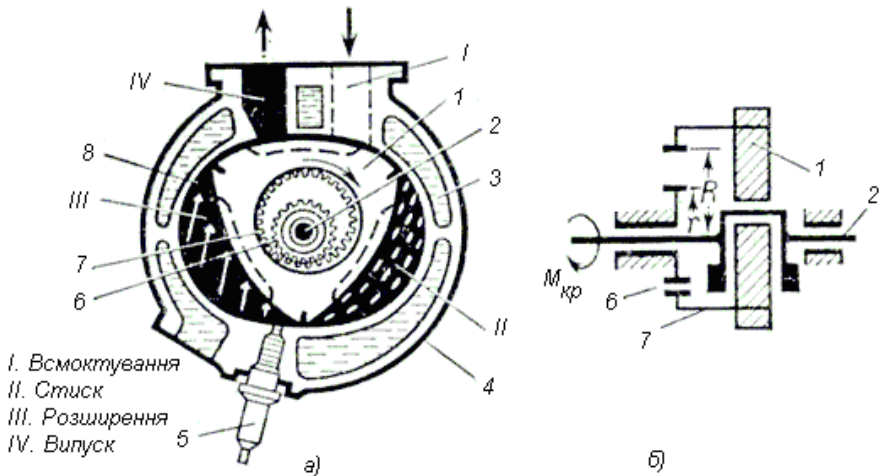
Схема роботи роторно-поршневого двигуна
